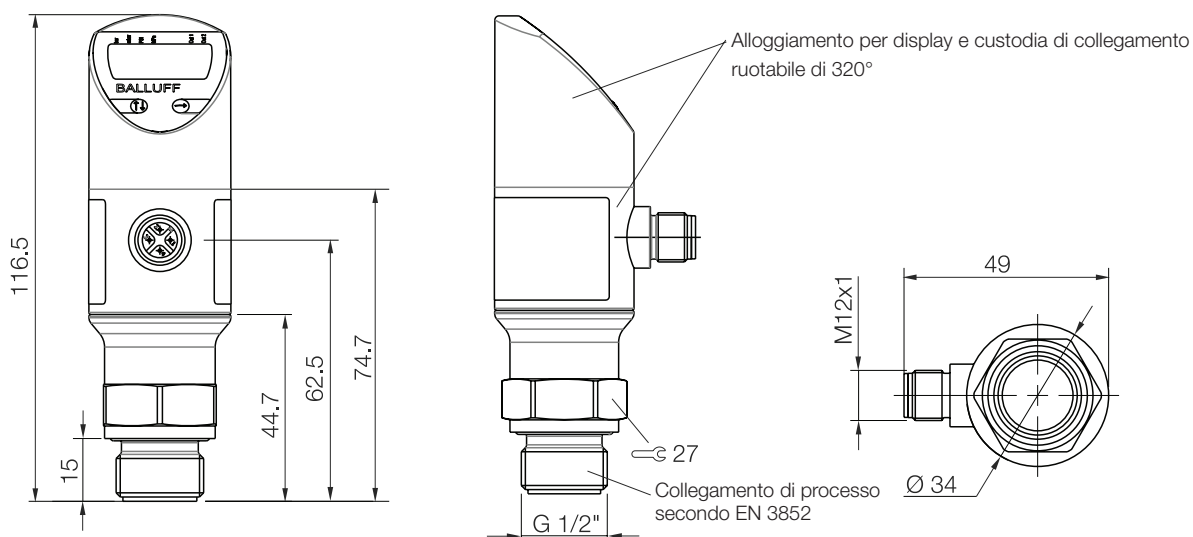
Disegno quotato sensore di pressione a filo sul lato frontale fino a 50 bar
